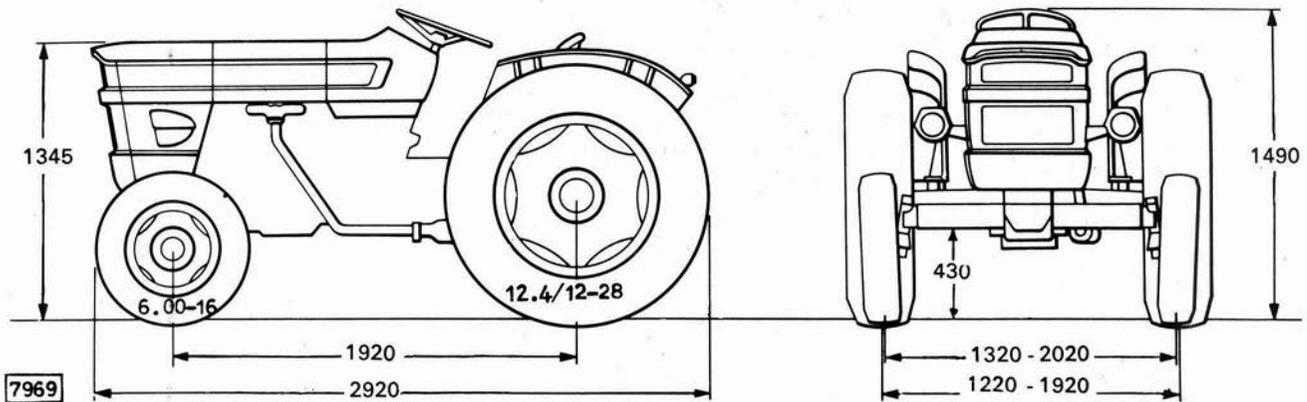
/1 - Dimensions d'encombrement du tracteur.
